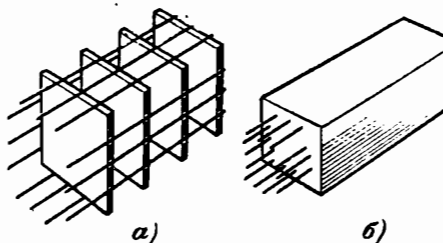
Сборка микромодуля. а — соединение плат; б — внешний вид модуля.
